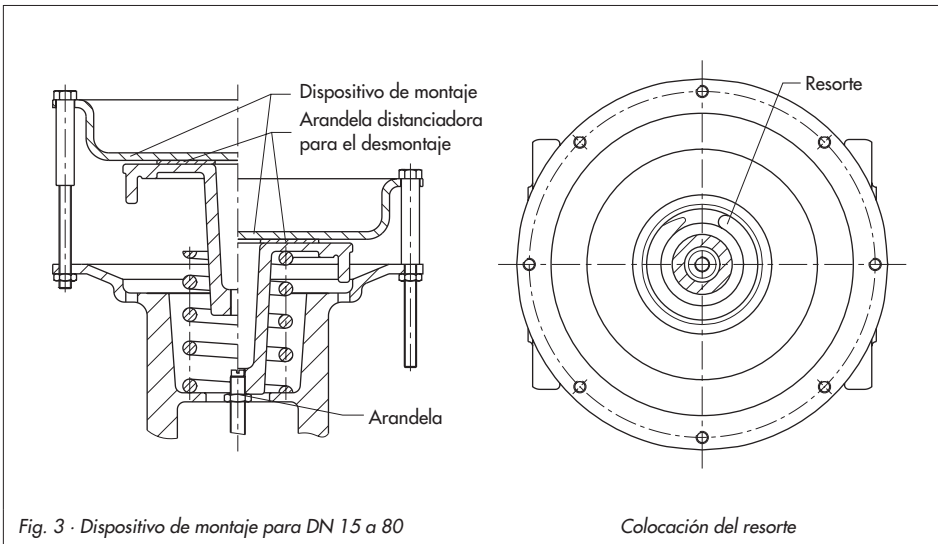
· Dispositivo de montaje para DN 15 a 80
